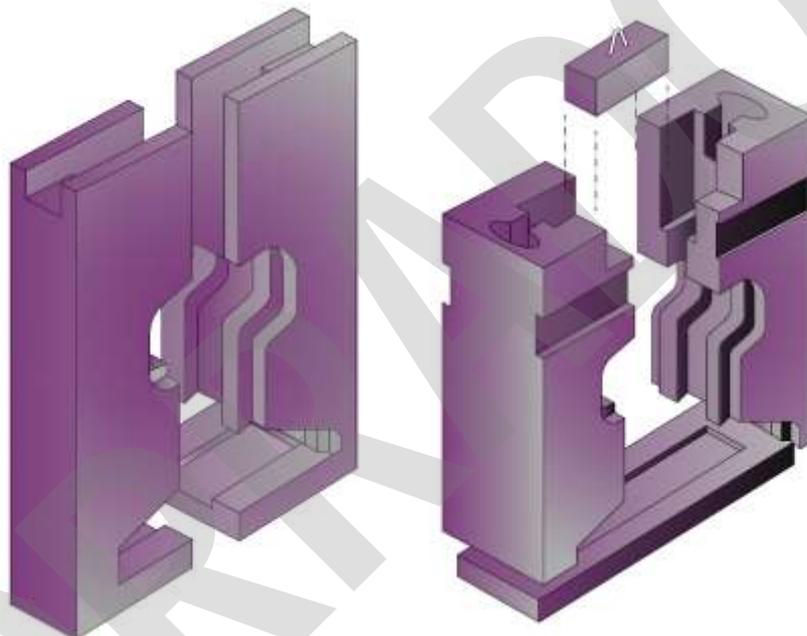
Esquema de moldes para soldadura aluminotérmica.
